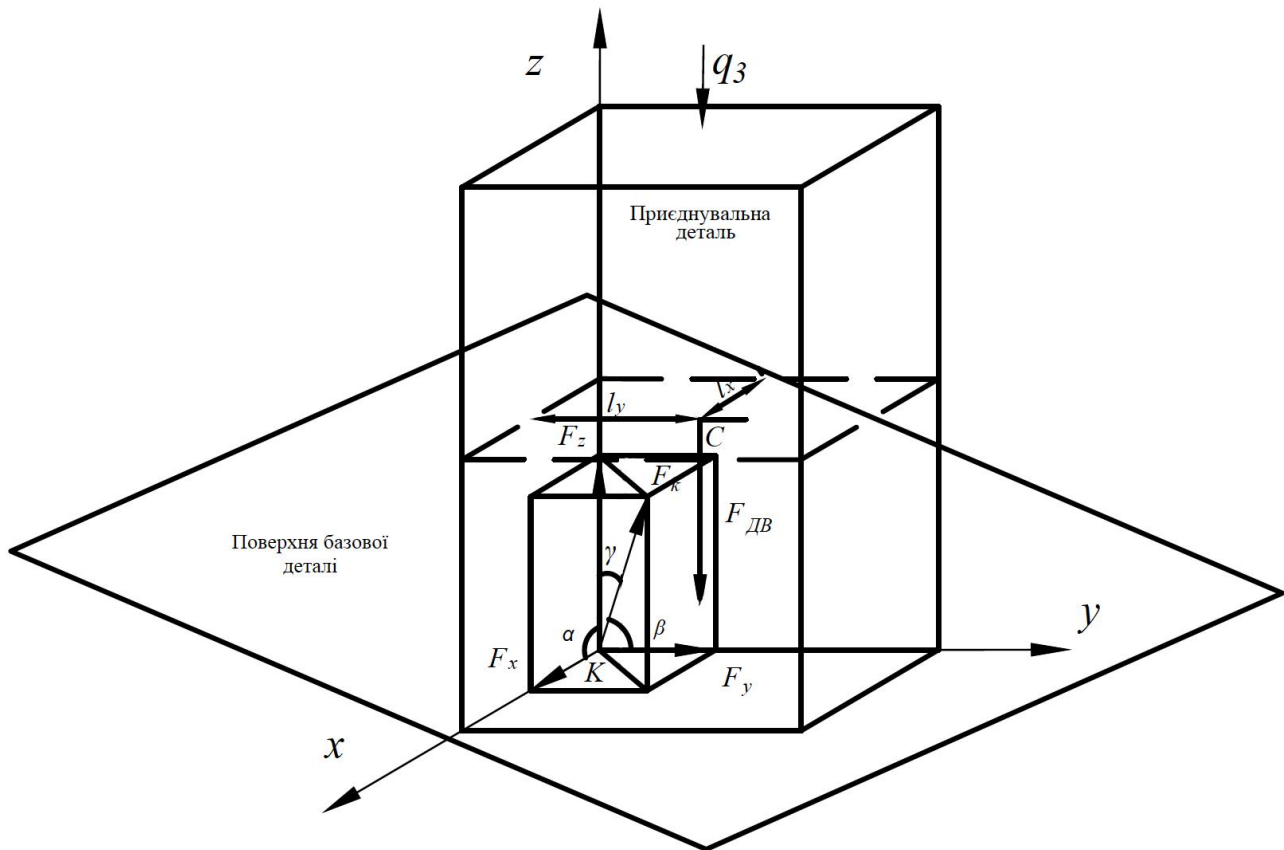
Схема сил, що діють на приєднувану деталь при контакті з поверхнею базової деталі
